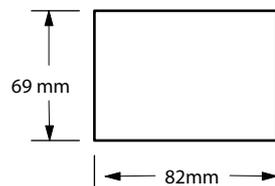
Dimensiones del recorte de montaje del TD 100C
